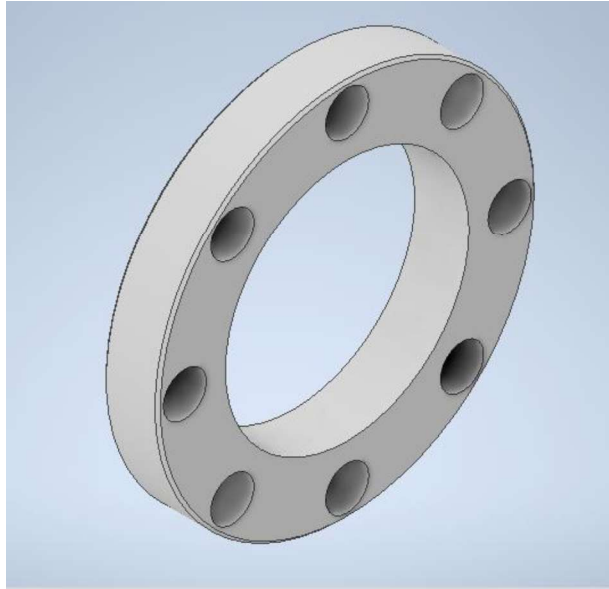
tampa do tubo e suporte do tubo de aquecimento
